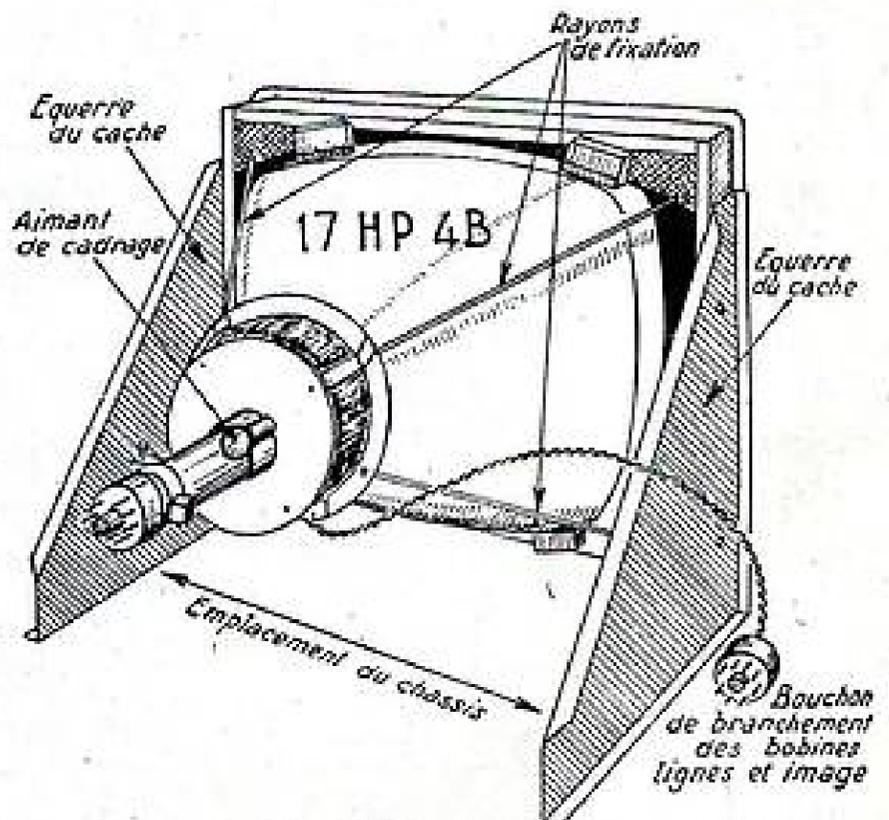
Le tube cathodique fixé sur son cache à équerres.
